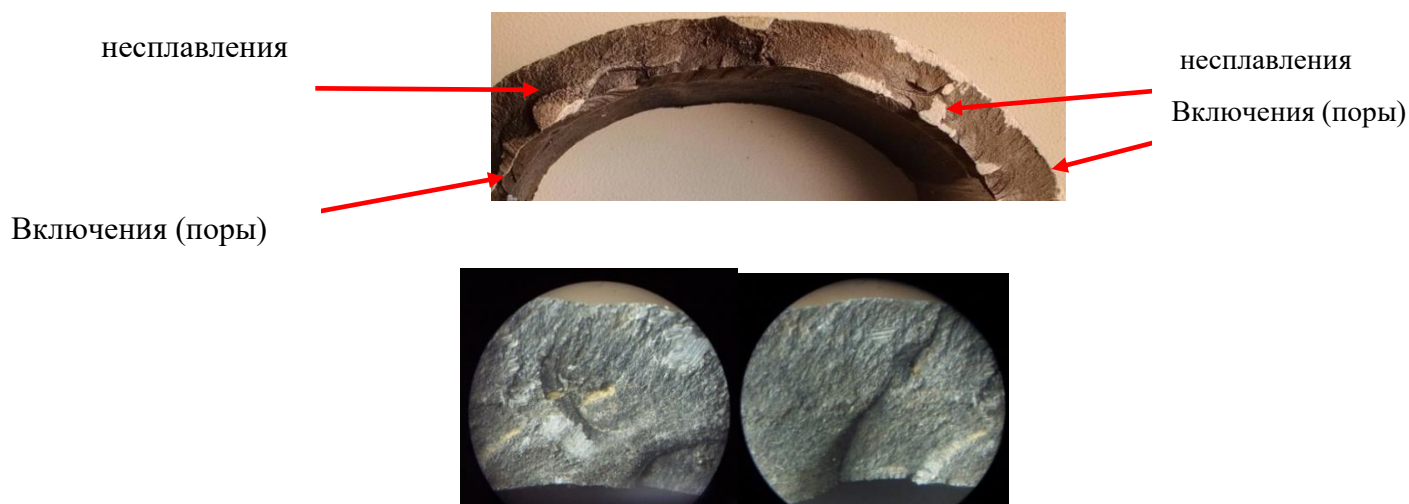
Дефекты в сварном соединении стояка отбора давления Ду 50
